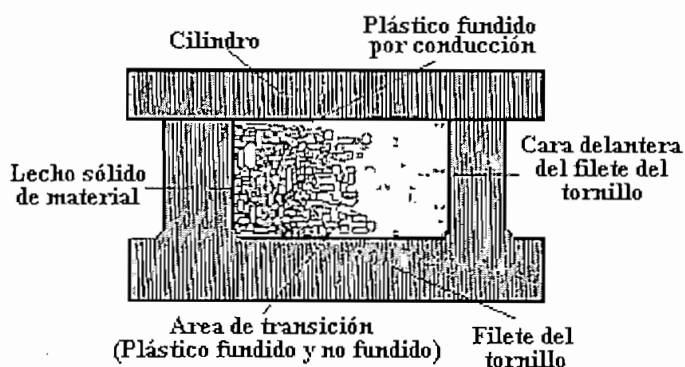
Diagrama del mecanismo de fusión en el canal del tornillo de extrusión.
